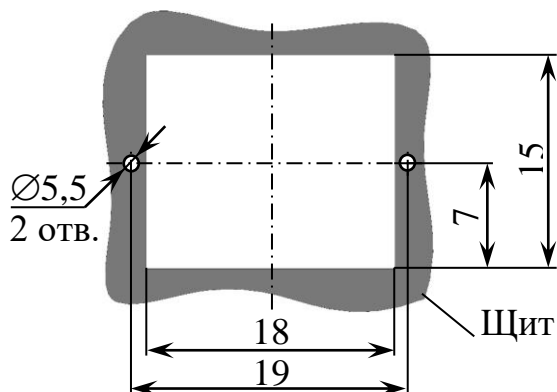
Расположение и размер отверстий для крепления блока преобразовательного VP79.01.100 (VP79.01.100-01)
